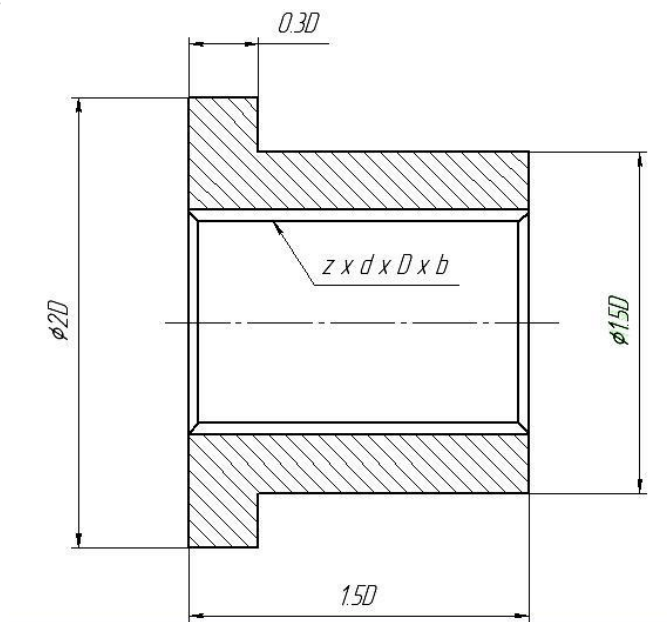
Втулка шліцьова (D – зовнішній діаметр шліців)
